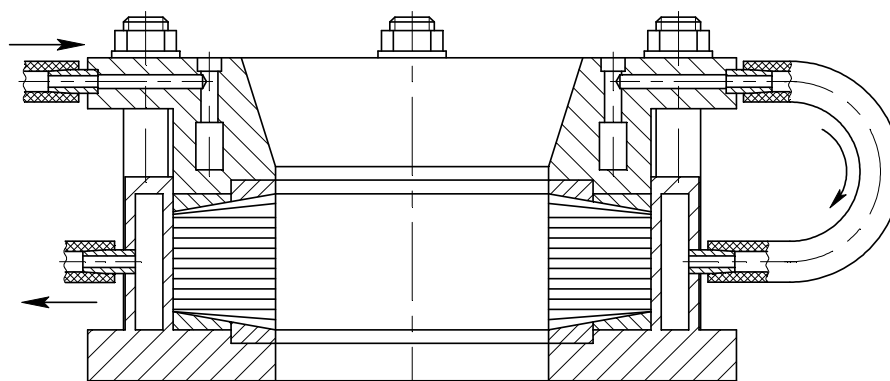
Водоохлаждаемое приспособление для сборки иглофрез
